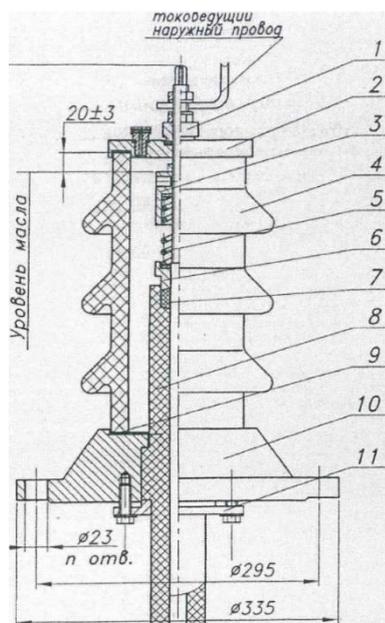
Фторопластовый изолятор проходной, модернизированный типа ИПФМ:
